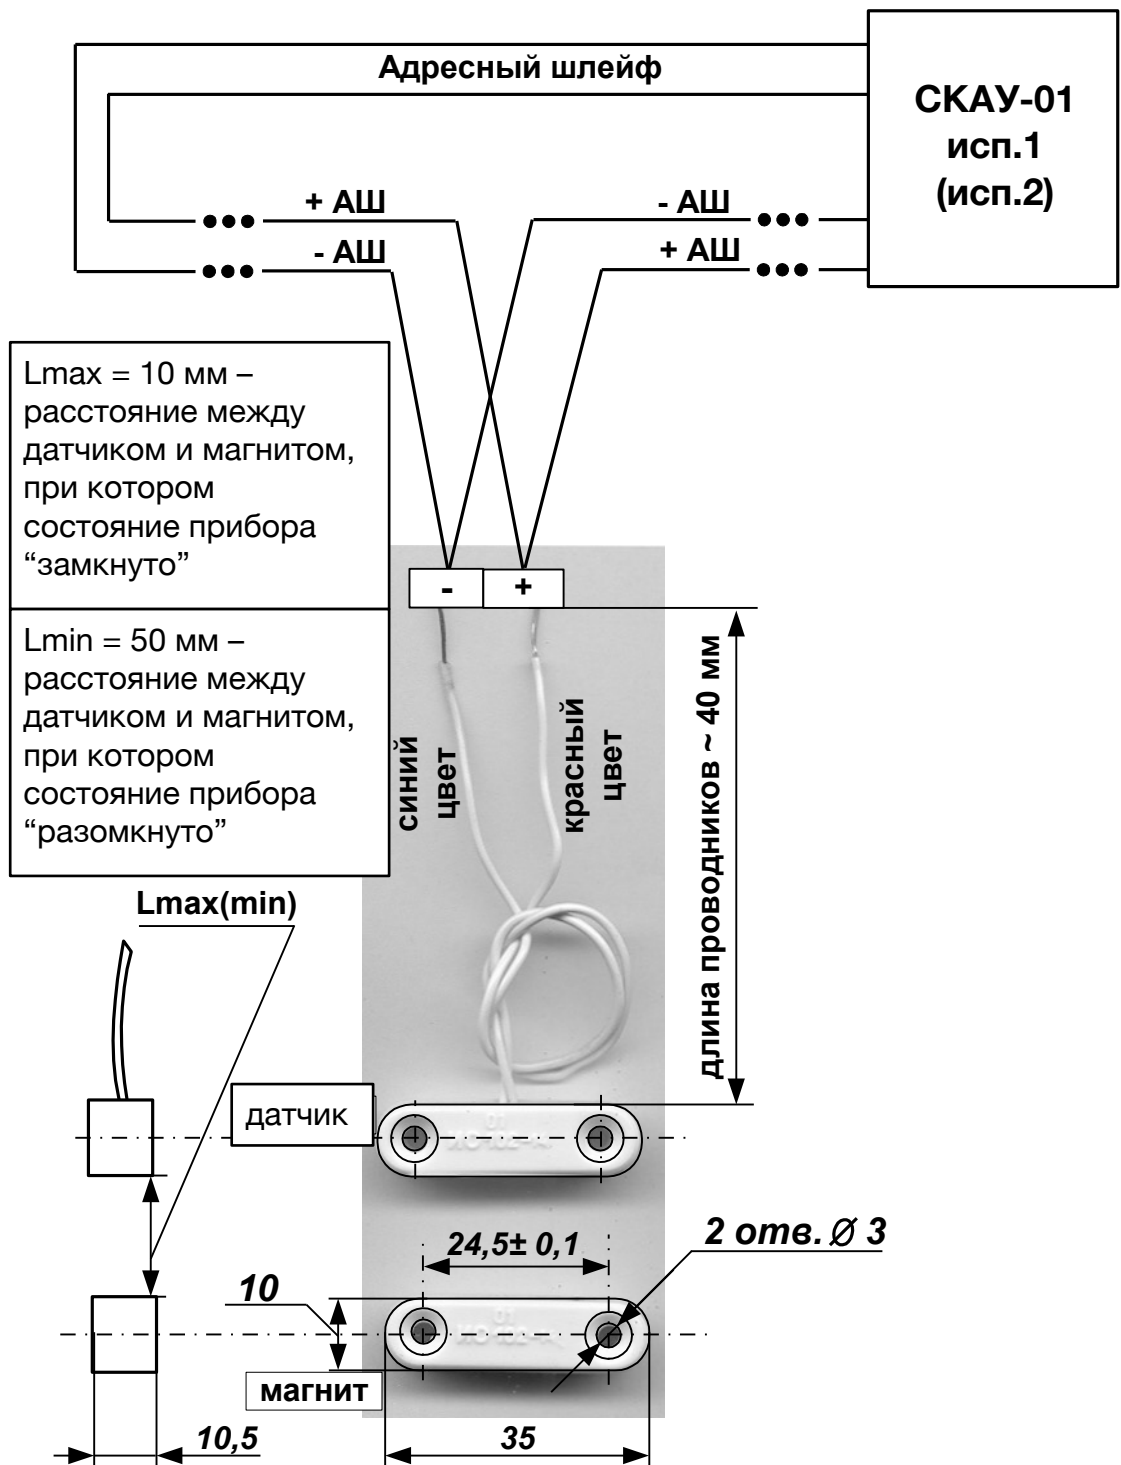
Конструкция, подключение, габаритные и присоединительные размеры
